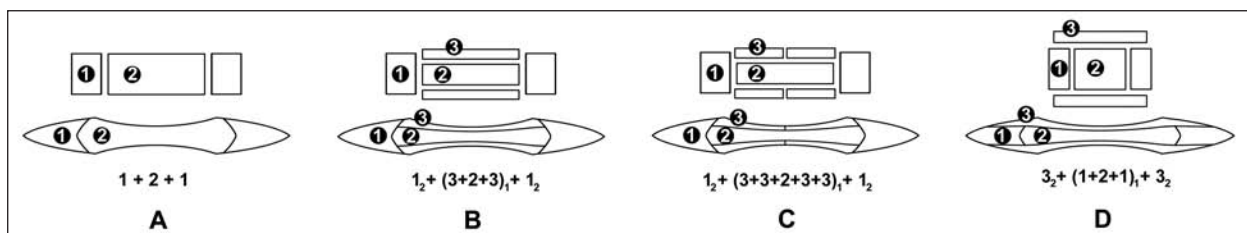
Металлографически определённые способы сварки заготовок при изготовлении клинков. По И. Гошеку
